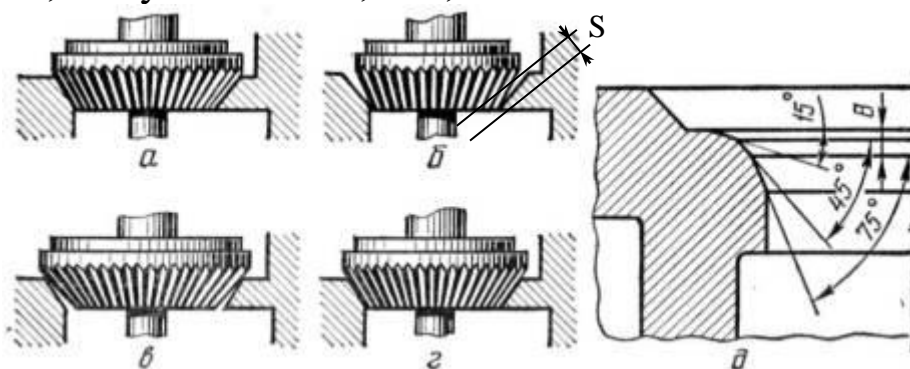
Ремонт клапанных гнезд фрезерованием: а - фрезой черновой  $45^\circ$ ; б - фрезой черновой  $75^\circ$ ; в - фрезой черновой  $15^\circ$ ; г - фрезой чистовой  $45^\circ$ ; д - схема образования рабочей фаски гнезда при фрезеровании; В - ширина рабочей фаски.
